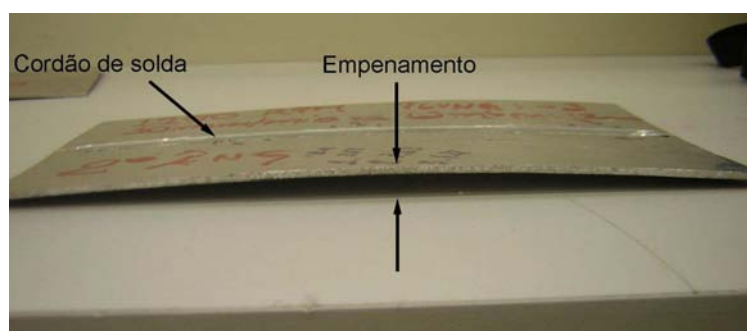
Empenamento apresentado pelas chapas após a soldagem por FSW.
